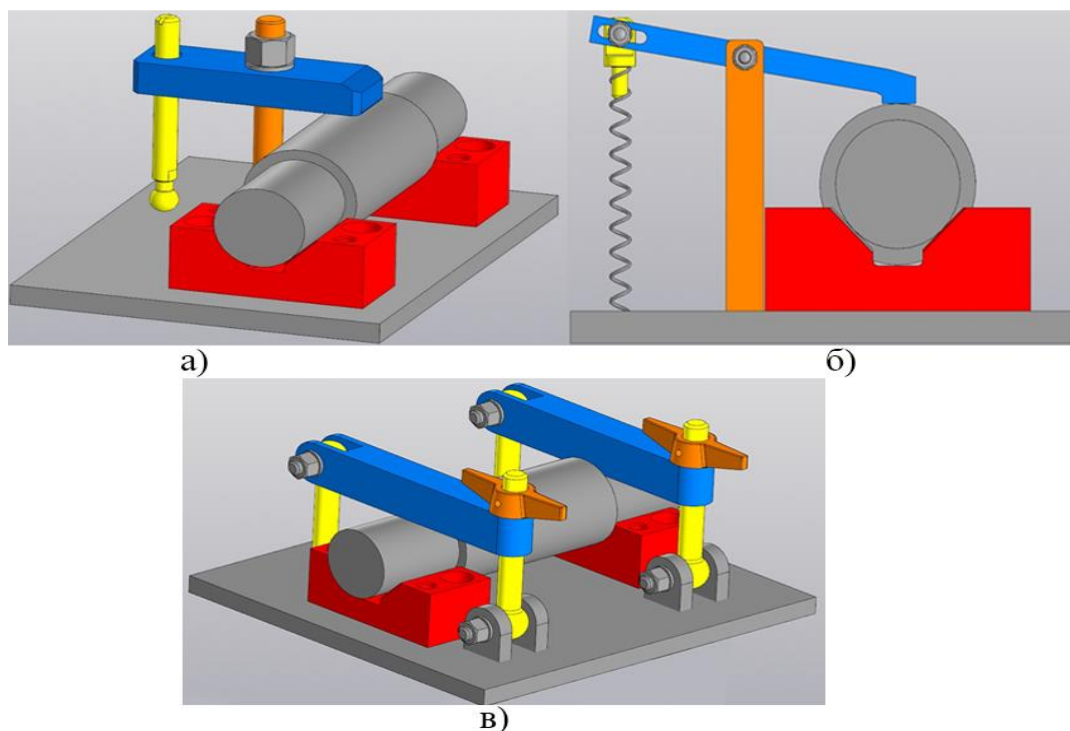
полученные конструкции приспособлений: а) с прихватом, б) с рычажным зажимом, в) с винтовым прихватом
